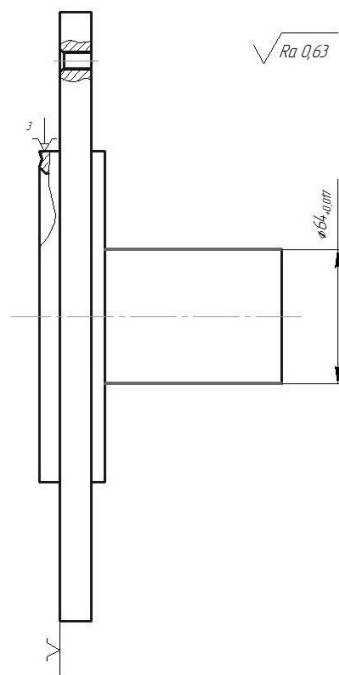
Фланець ведучої частини маточини колеса
